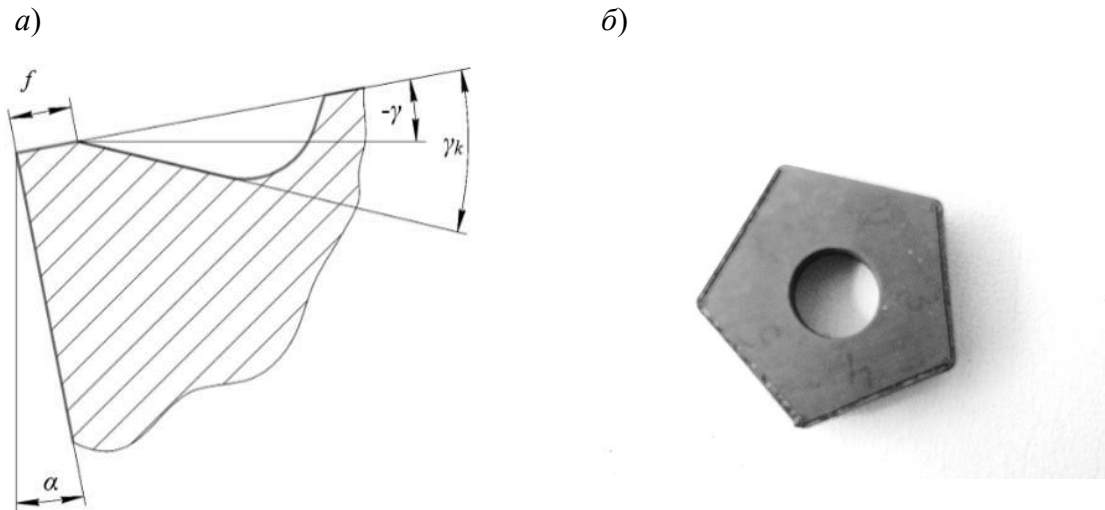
Схема канавки (а) и внешний вид пластины с канавками (б)
